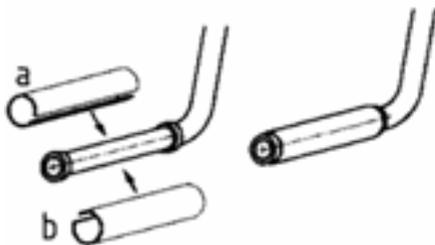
CORRECTA UNIÃO DE PORÇÕES DE RODA
